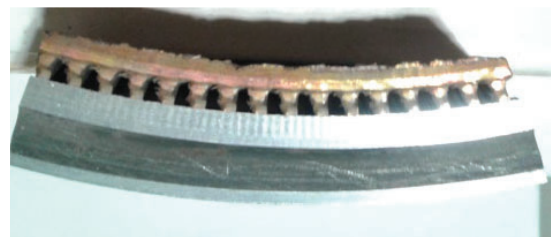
Профиль корпуса ЖРД с пазами для прохождения охлаждающей жидкости
